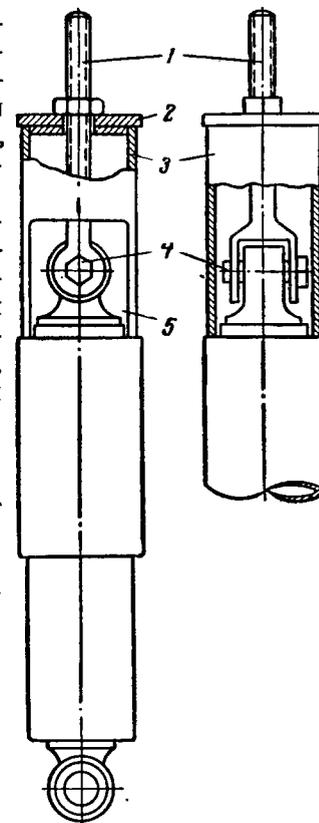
Приспособление для разборки подвески заднего колеса: 1 — выжимная вилка; 2 — верхняя опорная шайба; 3 — цилиндрический стакан; 4 — болт; 5 — двустороннее окно.
